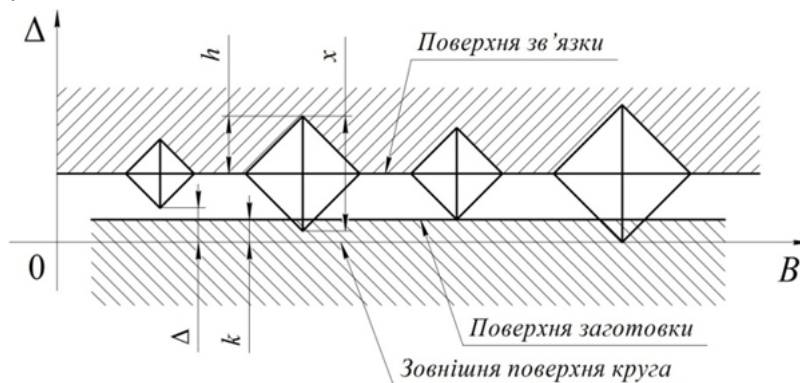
Взаємодія поверхні круга з поверхнею заготовки
